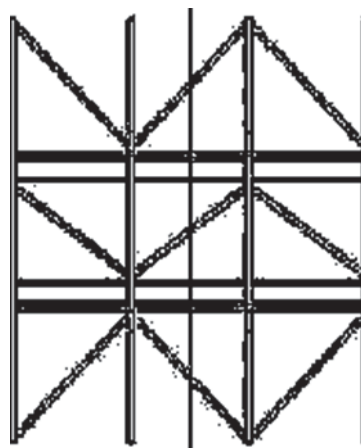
Bloco construtivo do componente (1) do rodado traseiro
